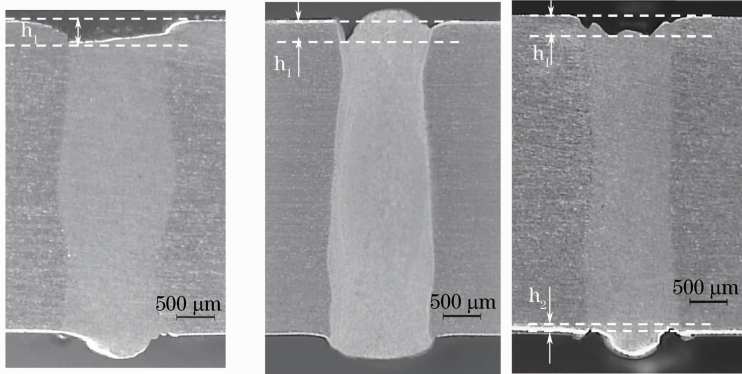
焊缝不同位置横截面形貌 ( $\Delta f=0, P=5 \text{ kW}, V=6.5 \text{ m/min}$ )
